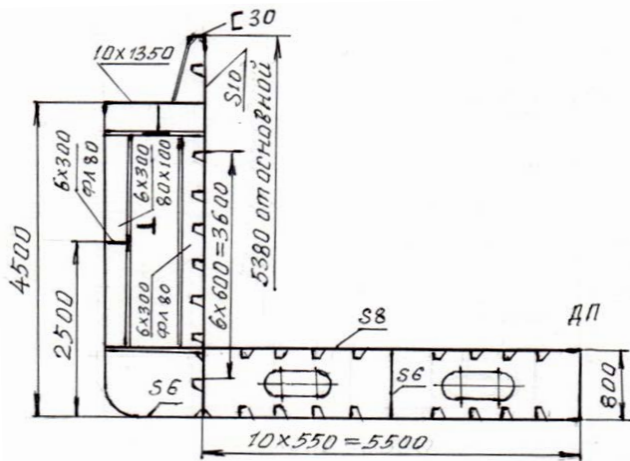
Вариант набора бортового перекрытия судна с двойными бортами
